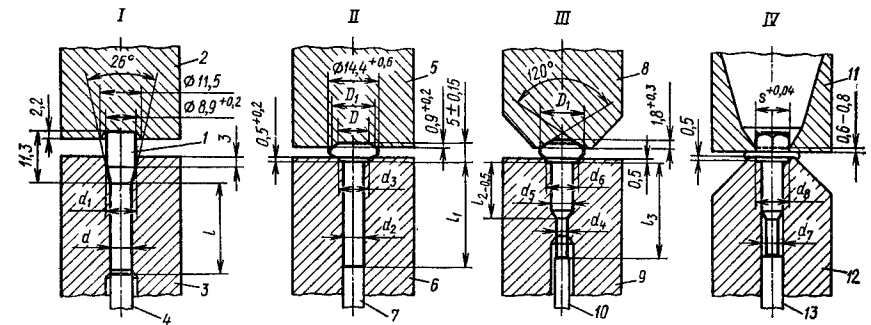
Переходы штамповки и рабочие части инструмента при четырехпозиционной высадке болтов М8 с формообразованием большой фаски на конце стержня:
